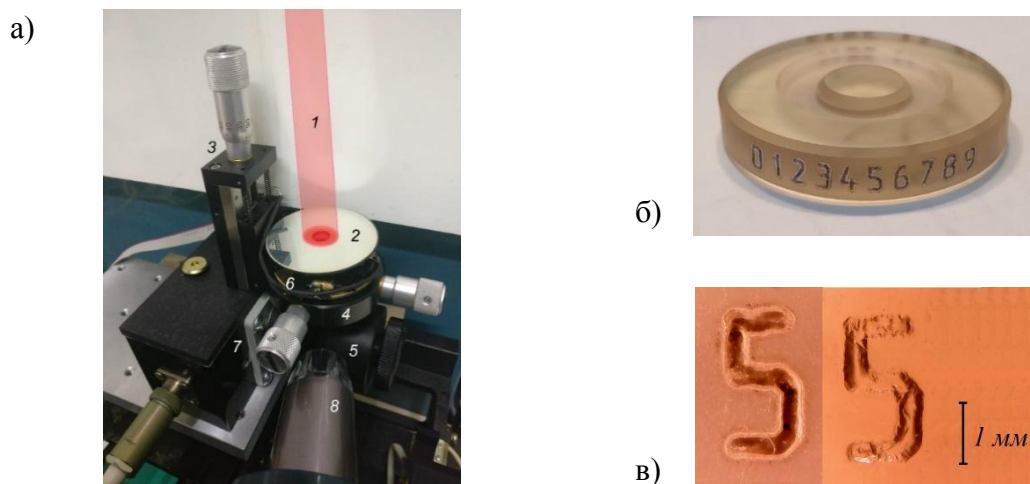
а) Общий вид рабочей зоны установки лазерной гравировки боковой поверхности ситалловой подложки (1 – излучение  $\text{CO}_2$  лазера; 2 – зеркало с алюминиевым покрытием; 3,4 – юстировочные устройства; 5 – держатель образцов; 6 – электромеханическое устройство двухкоординатного позиционирования расположенной на нем линзы из  $\text{ZnSe}$ ; 7 – шаговый двигатель для поворота образцов; 8 – цифровой микроскоп); б) пример лазерной гравировки; в) увеличенное изображение символа до и после химического травления.
